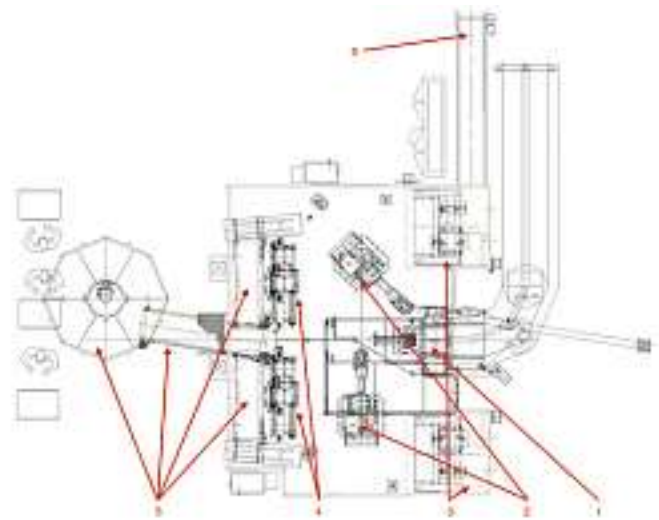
Flexible Bearbeitungszelle für Aluminium Ansaugrohre; deren Grundaufbau besteht aus:
